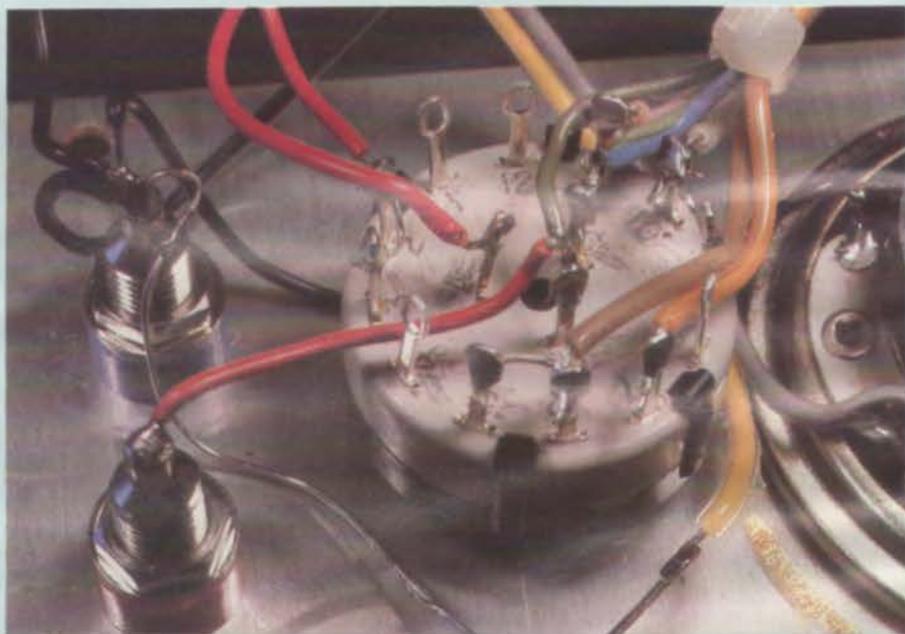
Gros plan sur le câblage du commutateur rotatif.
